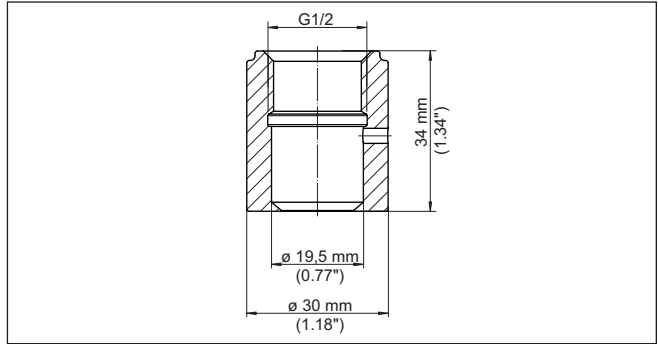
Dimensiones racor para soldar G $\frac{1}{2}$ (ISO 228-1) - Versión higiénica
